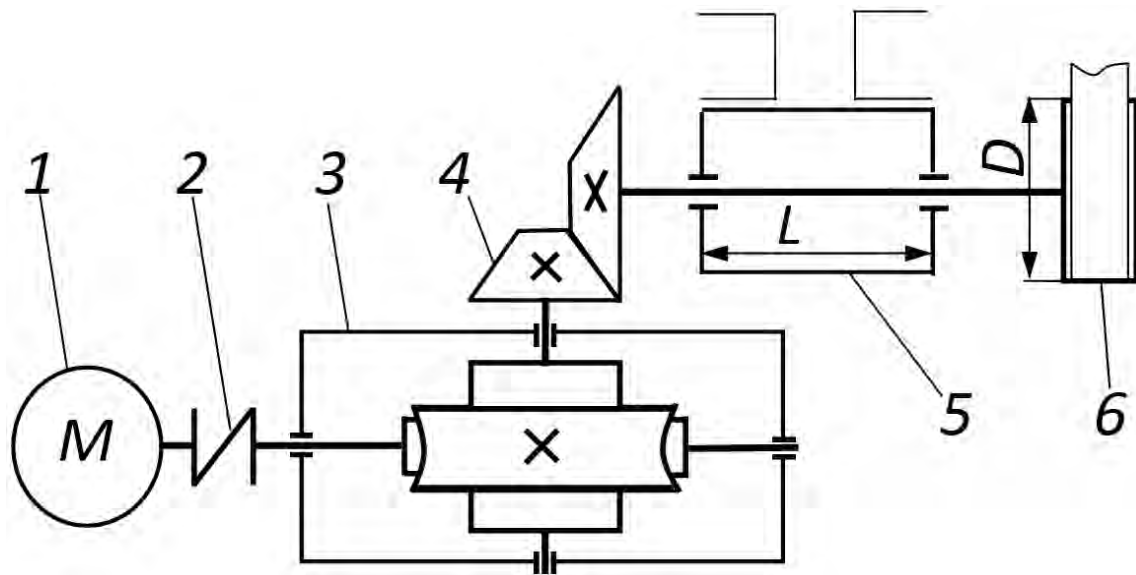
Схема привода тягового механизма (вид сверху): 1 – асинхронный электродвигатель; 2 – муфта упругая с резиновой звездочкой; 3 – редуктор червячный с нижним расположением червяка; 4 – открытая коническая прямозубая зубчатая передача; 5 – приводной вал, установленный в сборной опоре (стакане), имеющий крепление к вертикальной стойке; 6 – приводной шкив
